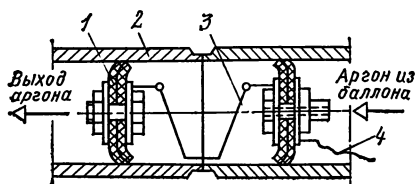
Узел сварки трубопровода в среде защитного газа:
